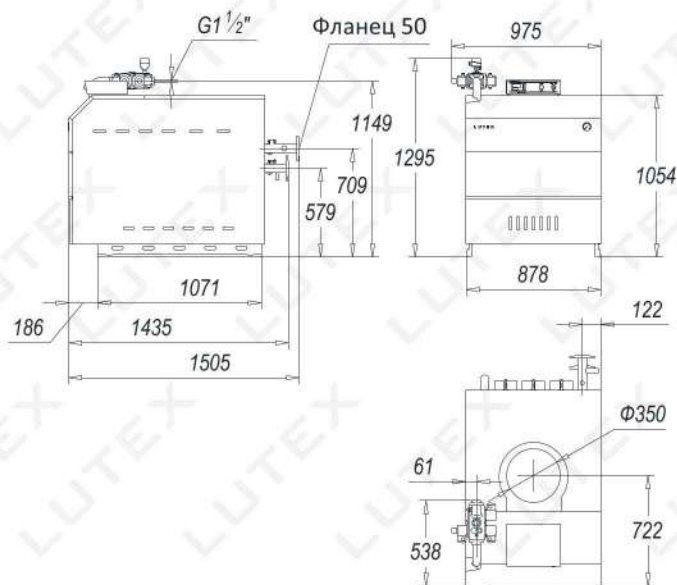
Габаритно – присоединительные размеры котла AR-S250.
